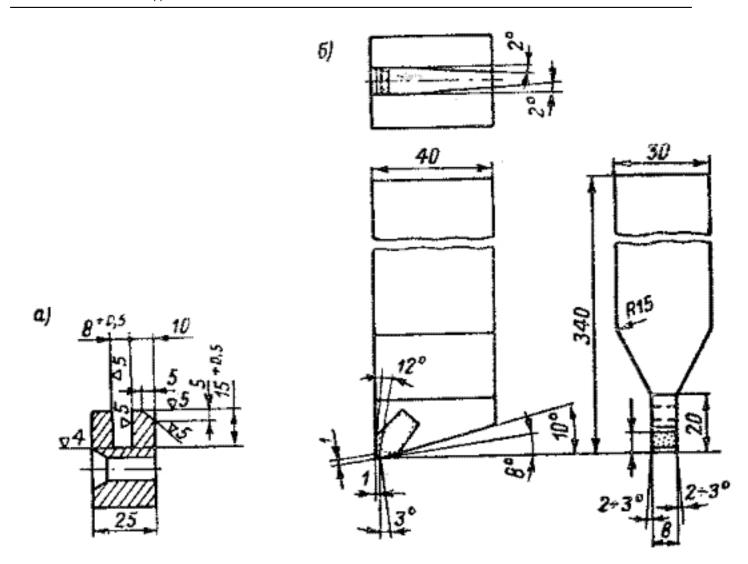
Применение прорезного резца: а — деталь; 6 — прорезной твердосплавный резец.
